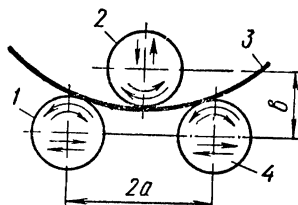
Схема гибки заготовки на копиравально-гибочном станке:
